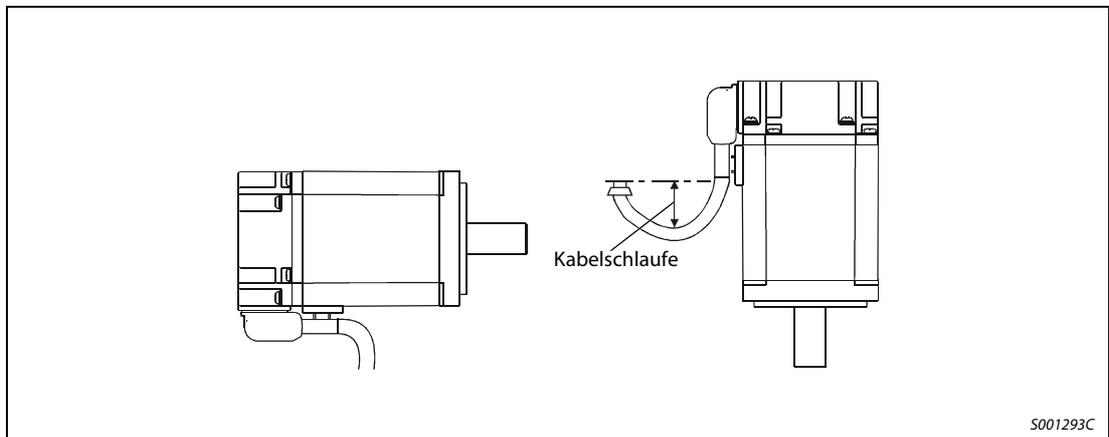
Montage des Servomotors horizontal oder vertikal mit Kabelschlaufe
